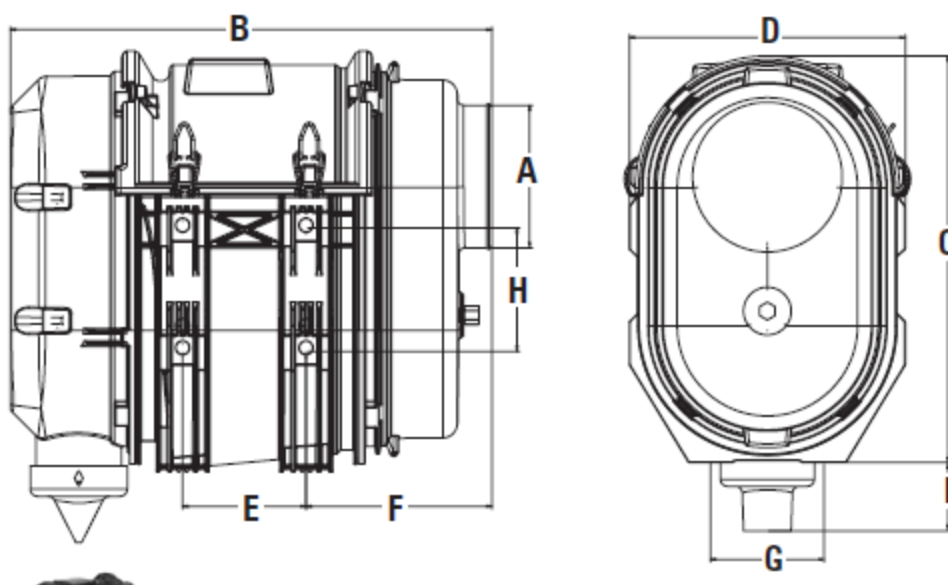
Desenho 2D computadorizado do conjunto filtro, pré-filtro e tampa fundida para proteção
